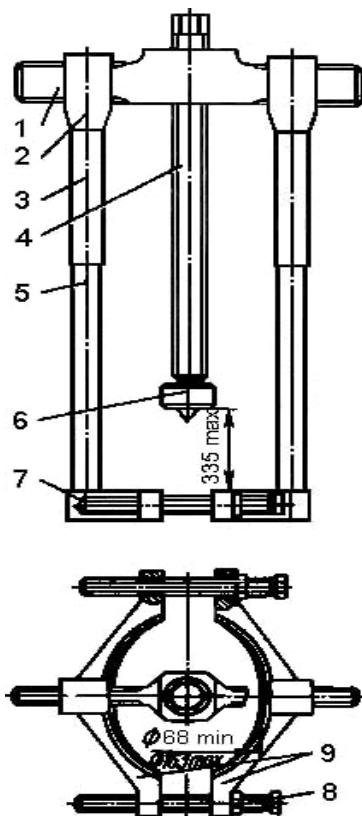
Съемник для снятия подшипников и шестерен раздаточной коробки:
